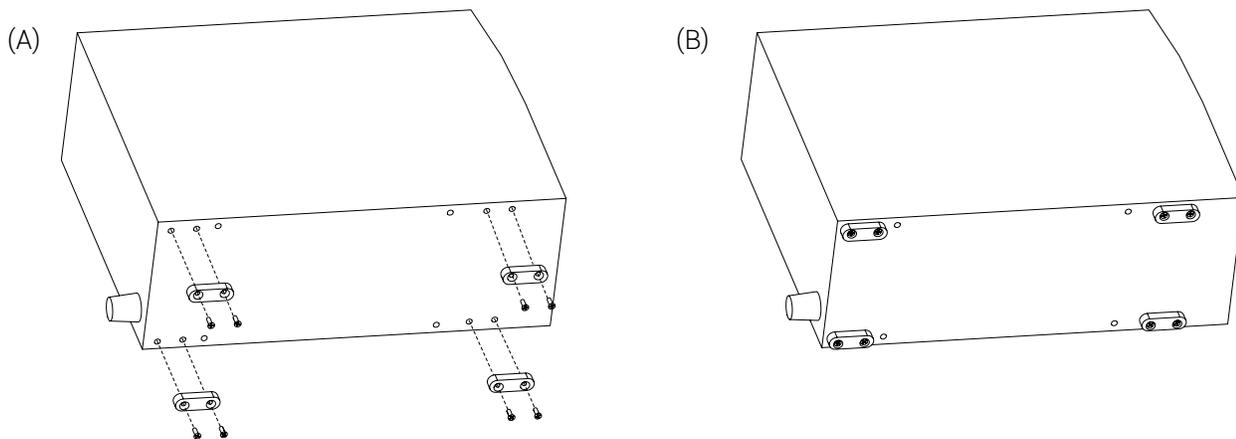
Pièces d'assemblage de l'unité ASC
